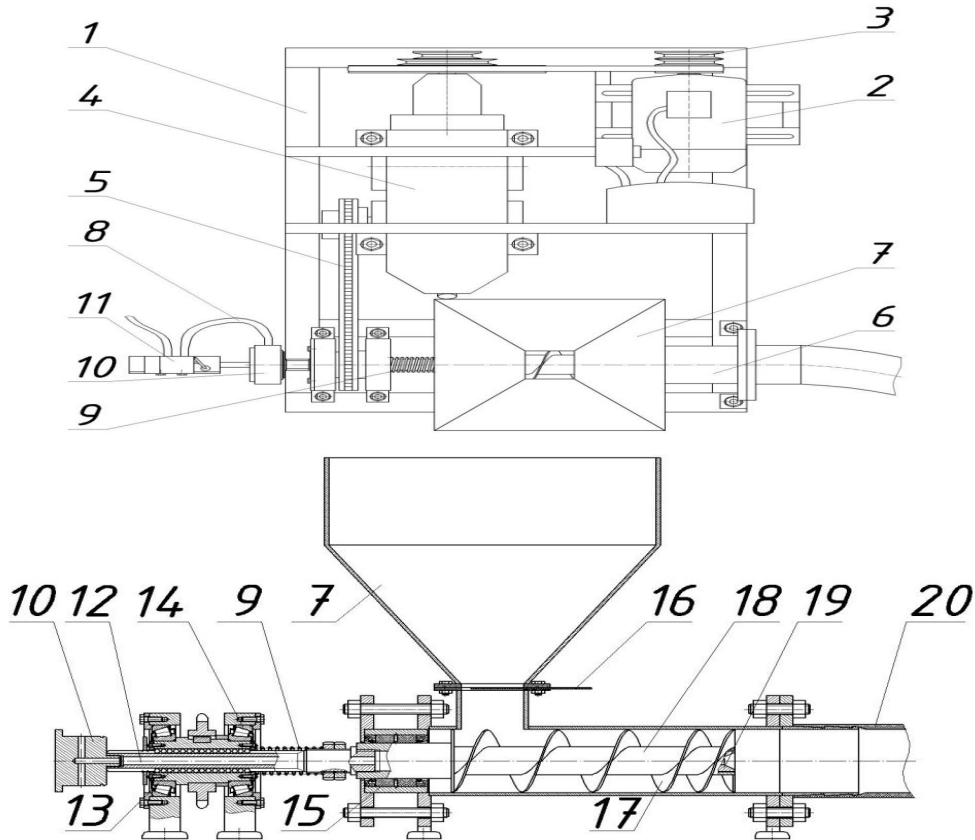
Шнековий пневмомеханічний транспортер (креслення) [4]:
